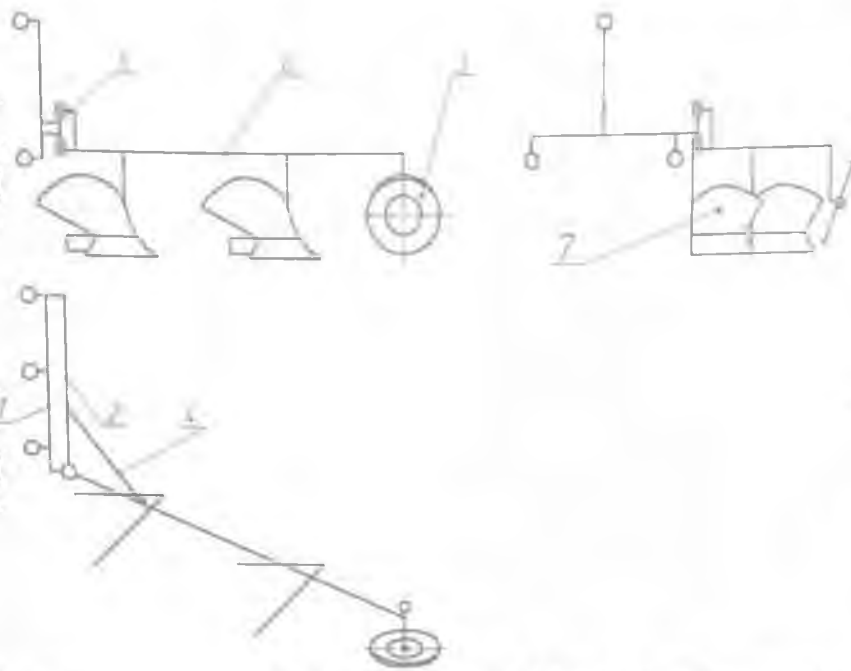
Принципова схема передньонапінного плуга: 1 - фронтальна рамка для приєднання; 2 - брус поперечини; 3 - опорне колесо; 5 - вертикальний шарнір; 4 - розтяжка; 7 - корпус; 6 - поздовжній брус рами плуга ПЛН-3-35
